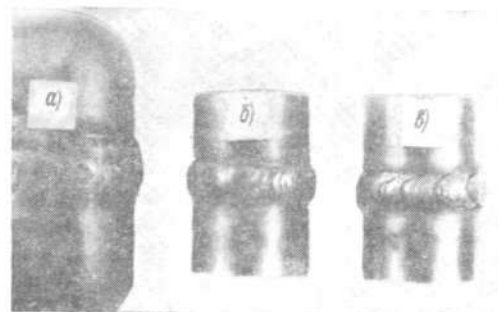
Внешний вид швов, выполненных ручной аргоно-дуговой сваркой с присадкой: а — многопроходный шов с хорошим формированием валиков; б — однопроходный шов с хорошим формированием валика; в — однопроходный шов с удовлетворительным (бугристым) формированием валика.
